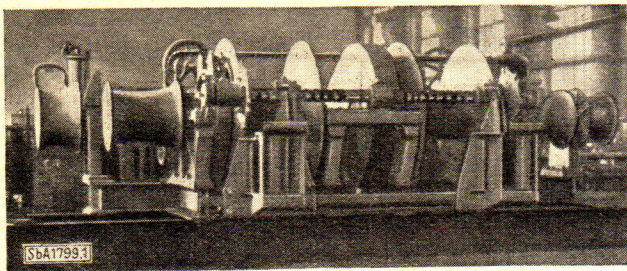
2,5-t-Fischnetzwinde für „Seiner“, alte Ausführung
